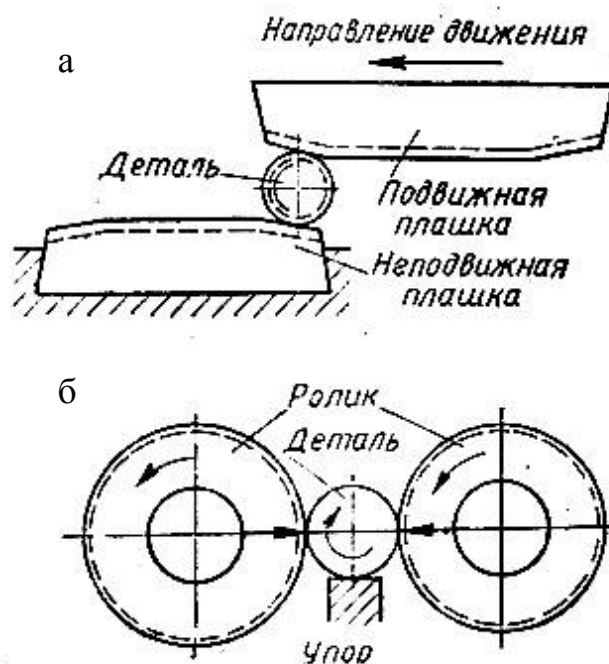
Схемы накатывания резьбы плашками (а) и роликами (б)
